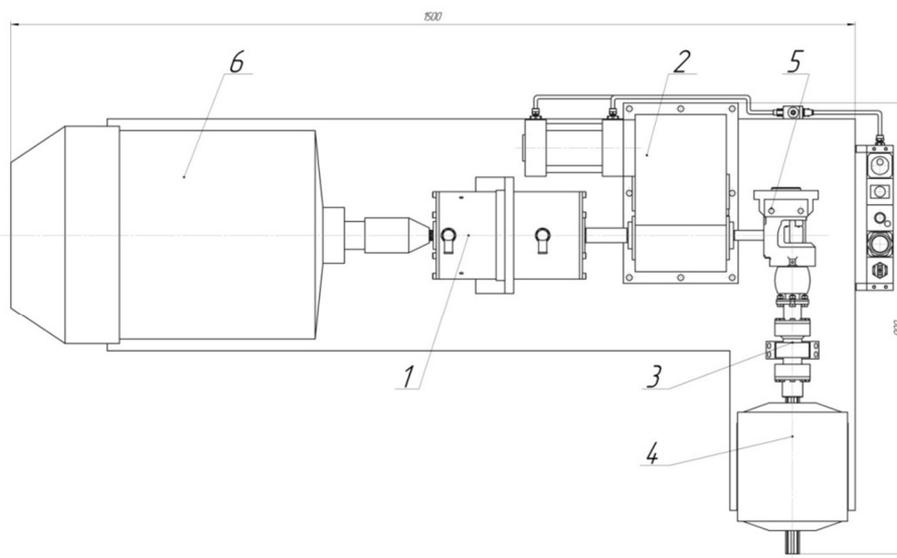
Общий вид испытательного стенда: 1 – муфта сцепления-торможения; 2 – реверс-коробка передач; 3 – датчик крутящего момента М40; 4 – порошковая муфта ПТ16М1; 5 – испытуемый редуктор; 6 – электродвигатель АИР180М2
